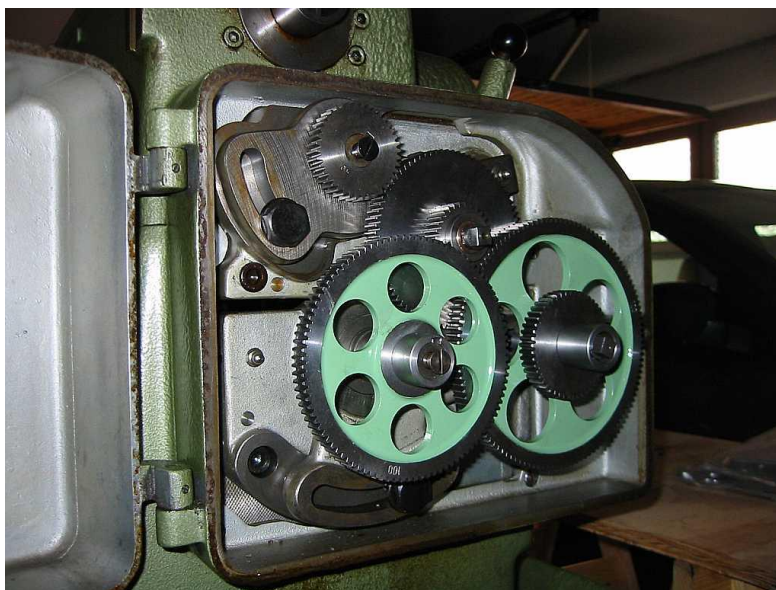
Getriebe und Wechselräder für Drehmaschine Schaublin SV 102 [54]
